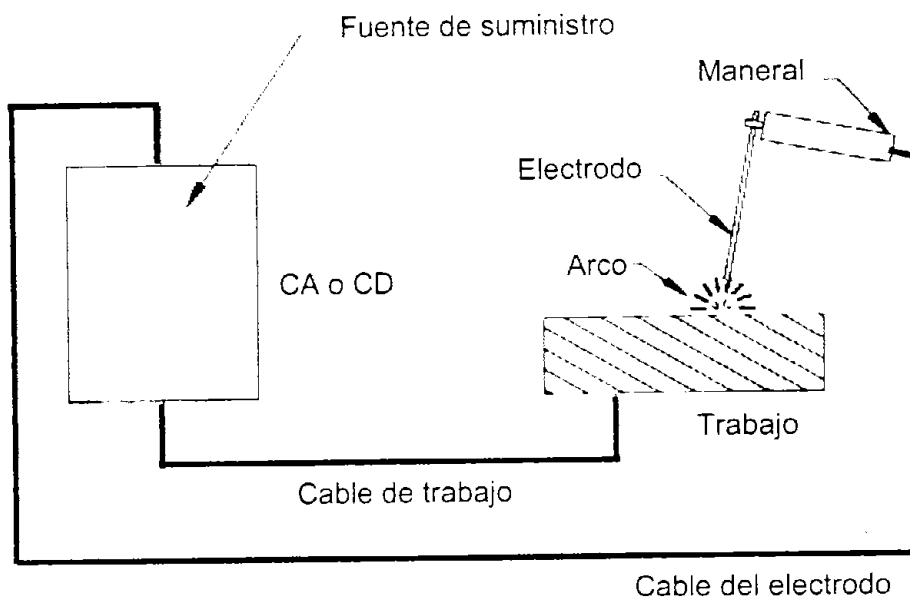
Circuito de la soldadura por arco metálico con electrodo revestido.
